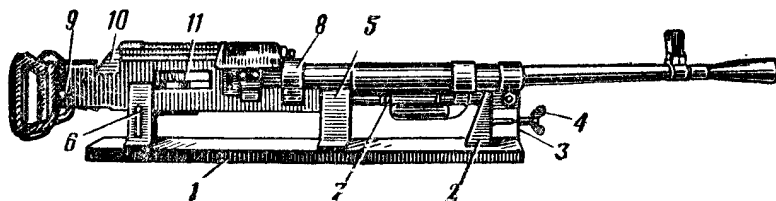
Станок для показа работы частей и механизмов станкового пулемета Горюнова:
